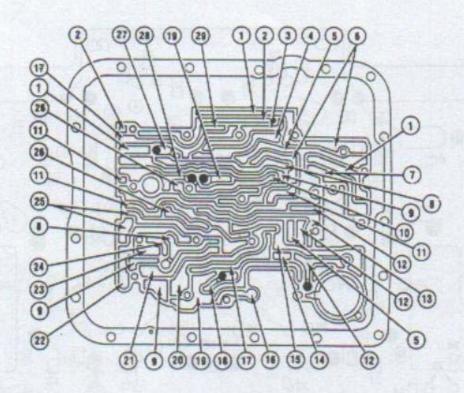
Gehäuse-Ölkanäle und Prüfkugel-Orte
